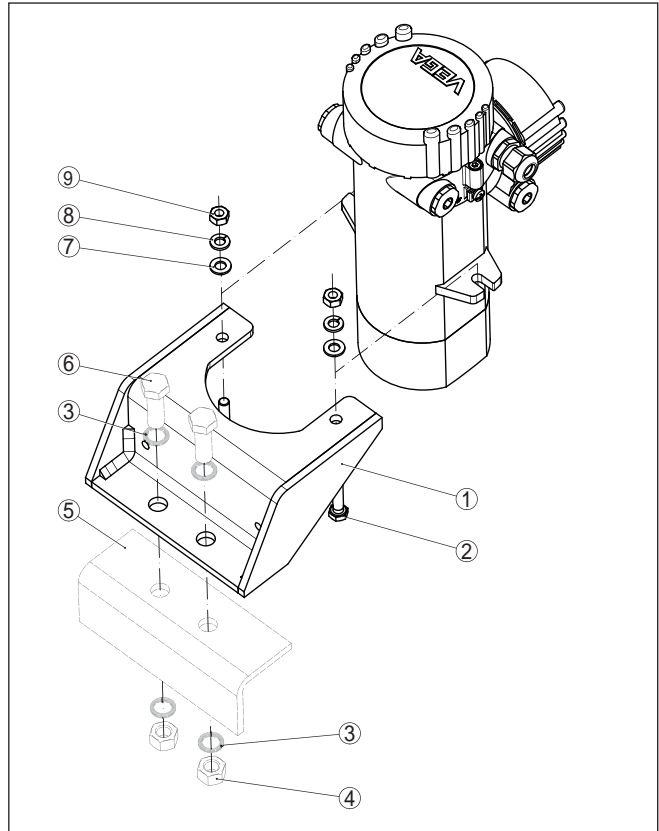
Montaje del adaptador de montaje (versión estándar)
